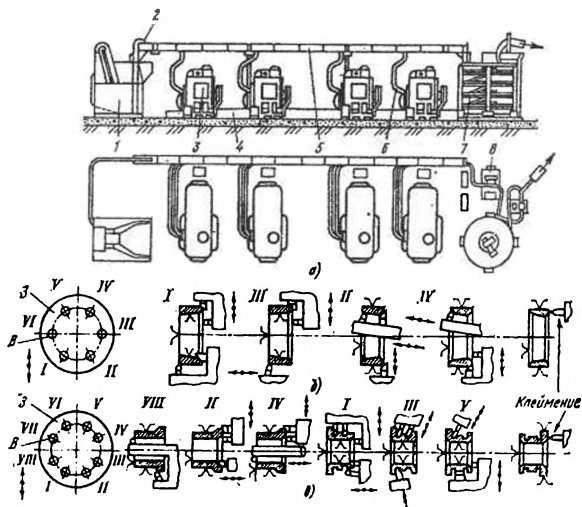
Автоматична лінія токарної обробки кілець підшипників:
